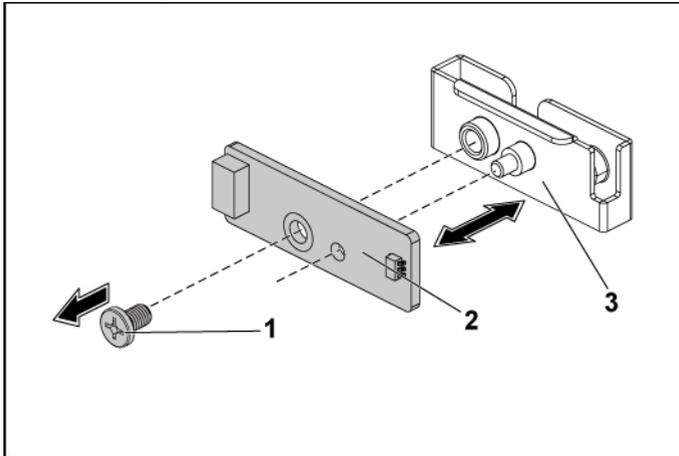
Sensorplattenbaugruppe entfernen und installieren
